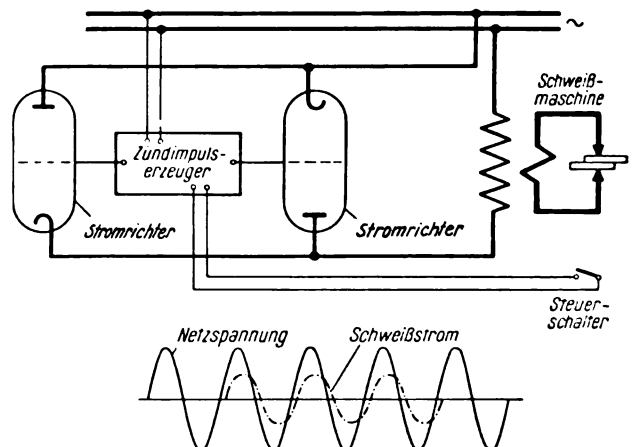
Grundsätzliches Schaltbild einer Schweißmaschine mit Schweißtaktter. Netzspannungs- und Schweißstromkurve bei 3 Perioden Schweißzeit
